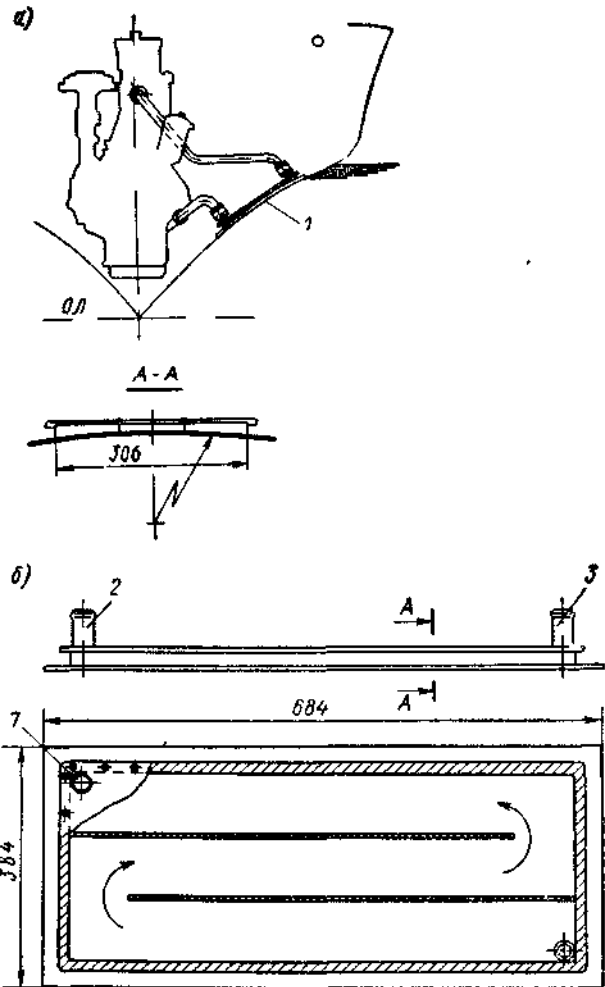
Пластинчатый забортный холодильник: а — схема установки холодильника на катере; б — конструкция холодильника.
